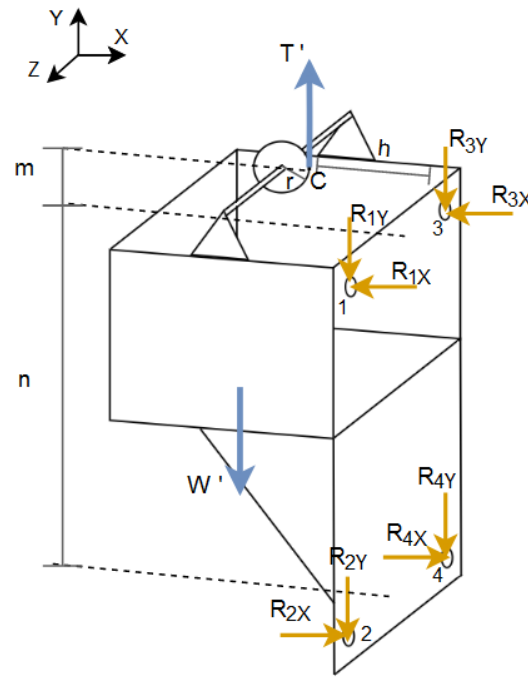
Cargas externas que actúan sobre el conjunto módulo de soporte – componentes mecánicos.
